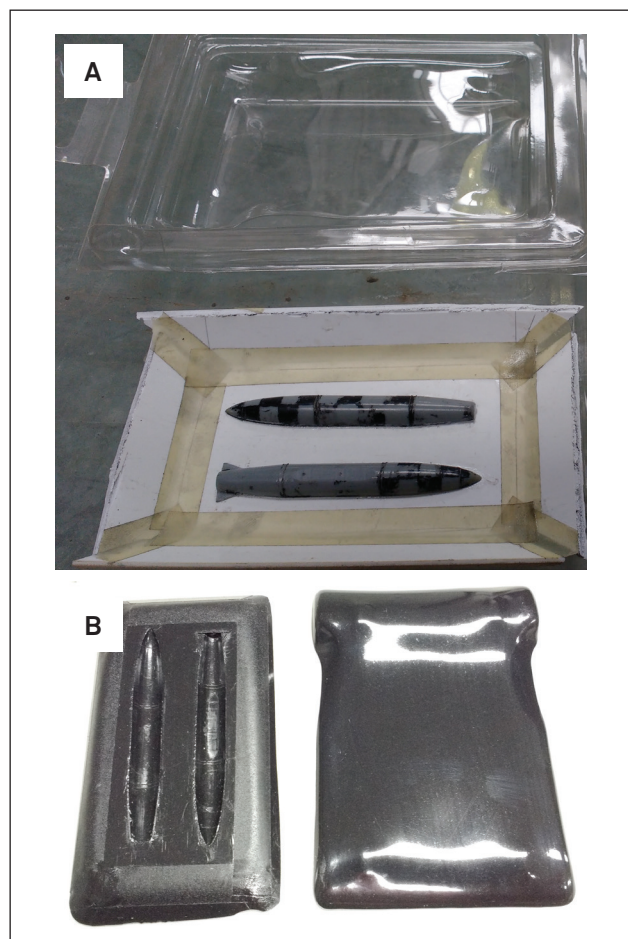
(A) Moldes de teste e (B) peças desmoldadas
